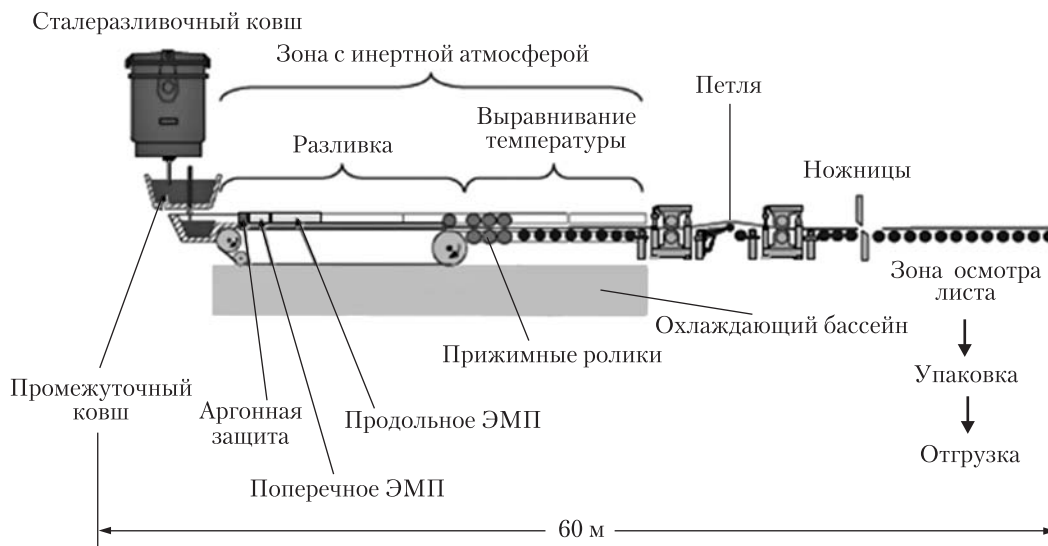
Схема горизонтальной разливки стали для получения тонкого листа по технологии Belt Casting Technology
